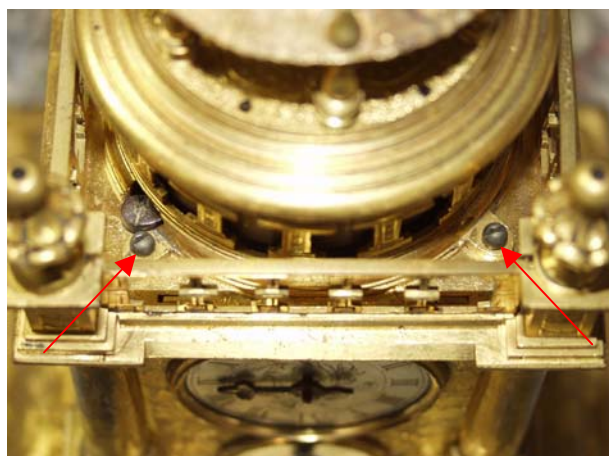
Festschraubens des Türmchenaufsatzes (vier Schrauben, wie die mit Pfeilen bezeichneten)
